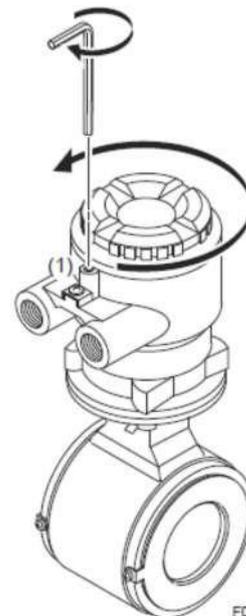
Remoção da Tampa da Caixa de Terminal (Sensor Remoto)
